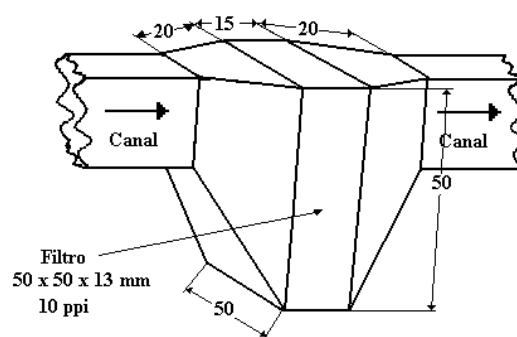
6 Forma y dimensiones de la cámara de filtrado utilizada (dimensiones en mm).
